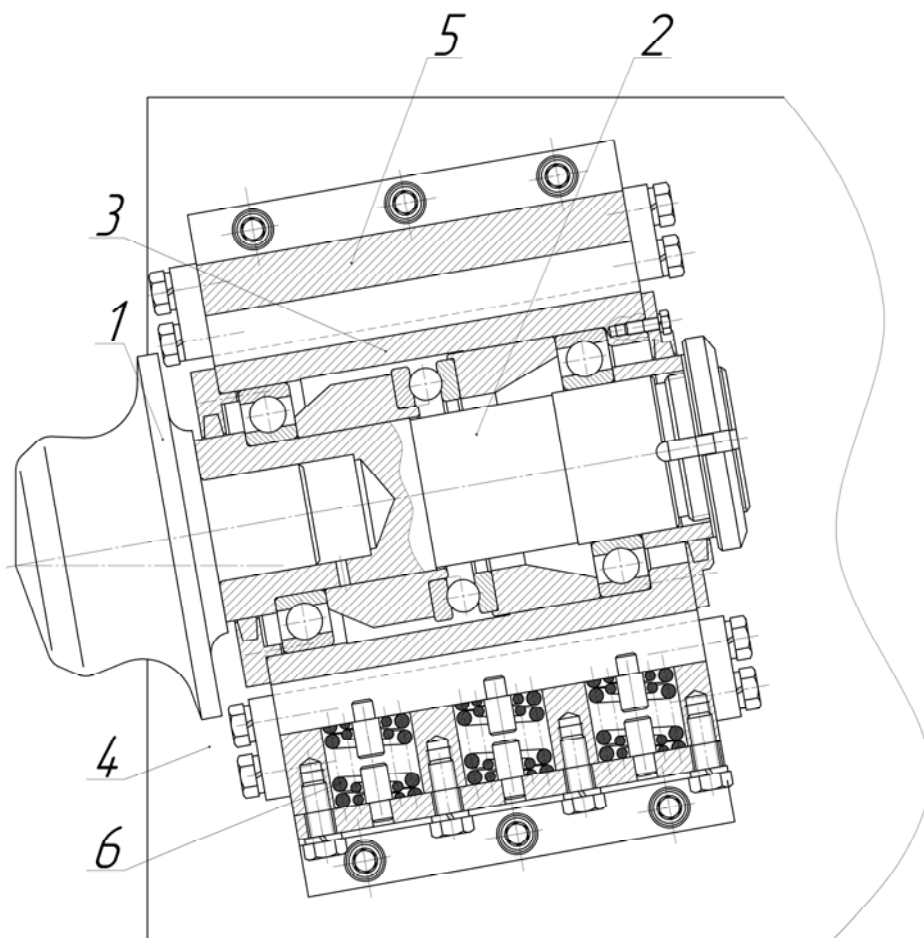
Складальне креслення розкочувального пристрою до лоботокарного верстата ЛТ2
